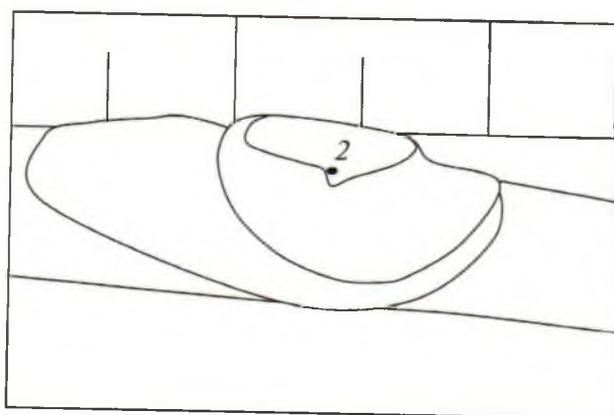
Пора в стыковом сварном соединении трубопровода. Дефект заметен после удаления избыточной выпуклости сварного шва абразивным инструментом
